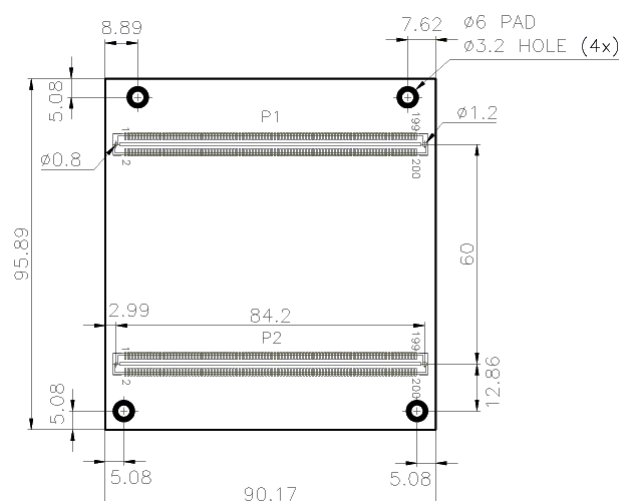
Plan avec les dimensions d'un PCB, vue du dessus [2]
